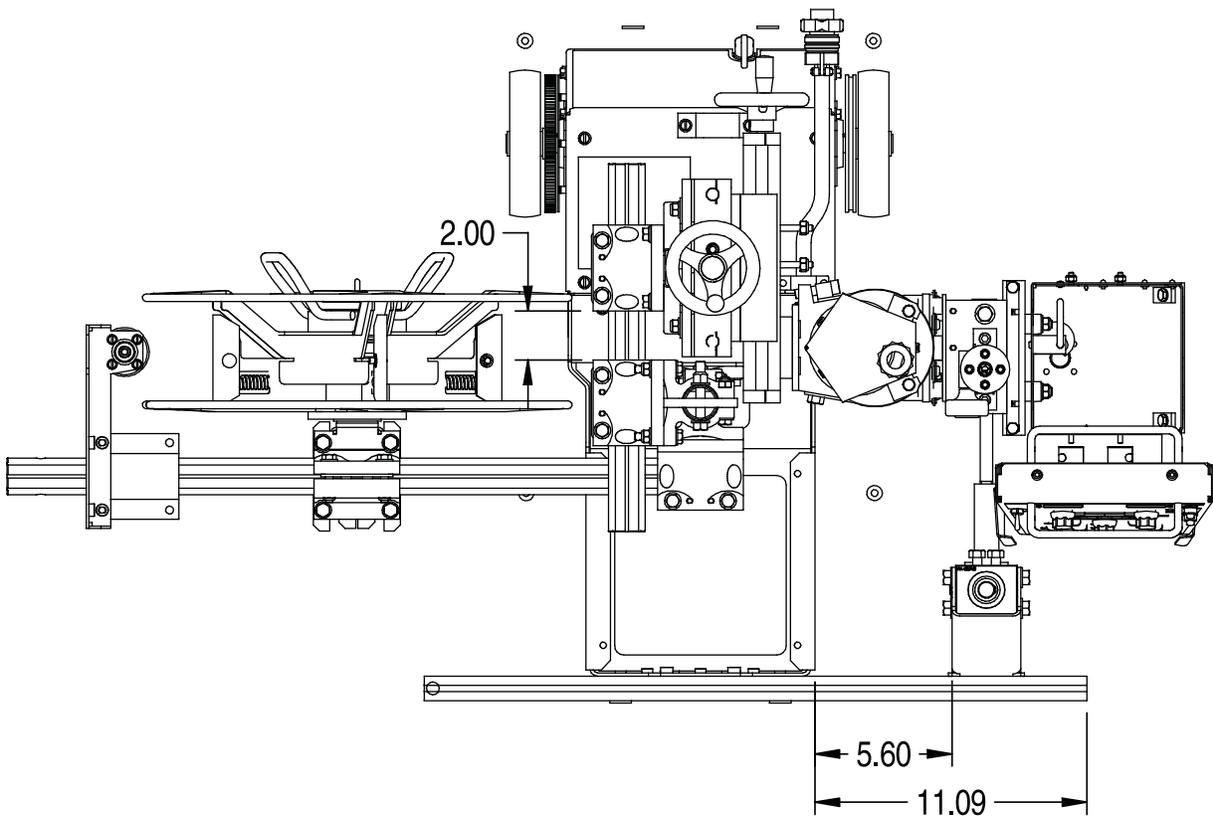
VISTA SUPERIOR DE LA SOLDADURA DE TUBERÍAS
